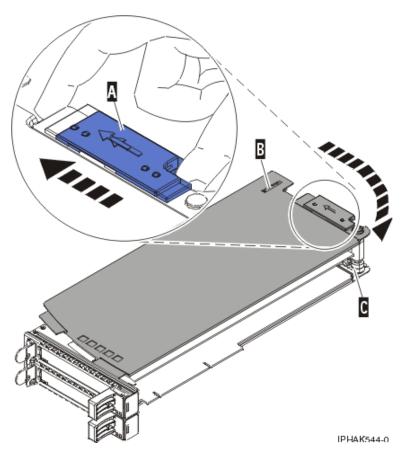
Retrait du couvercle de la cassette de cartes PCI
